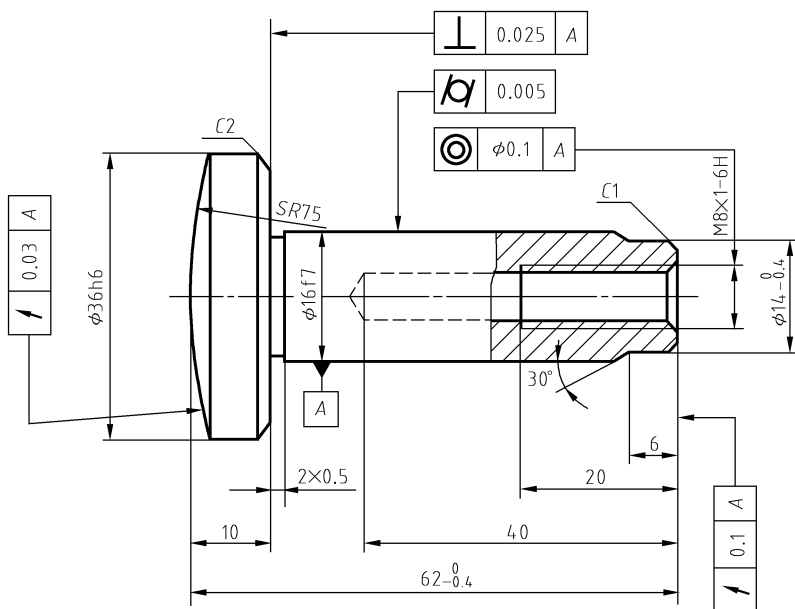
气门阀杆零件图几何公差标注示例
